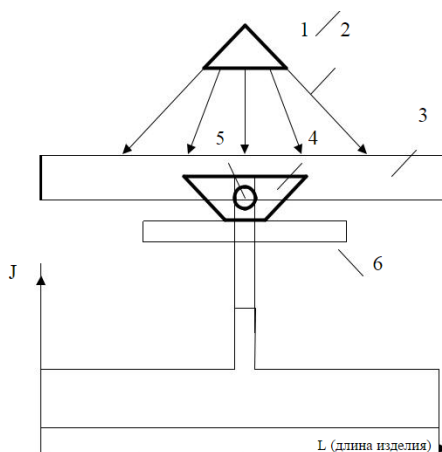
Схема просвечивания сварного соединения:
